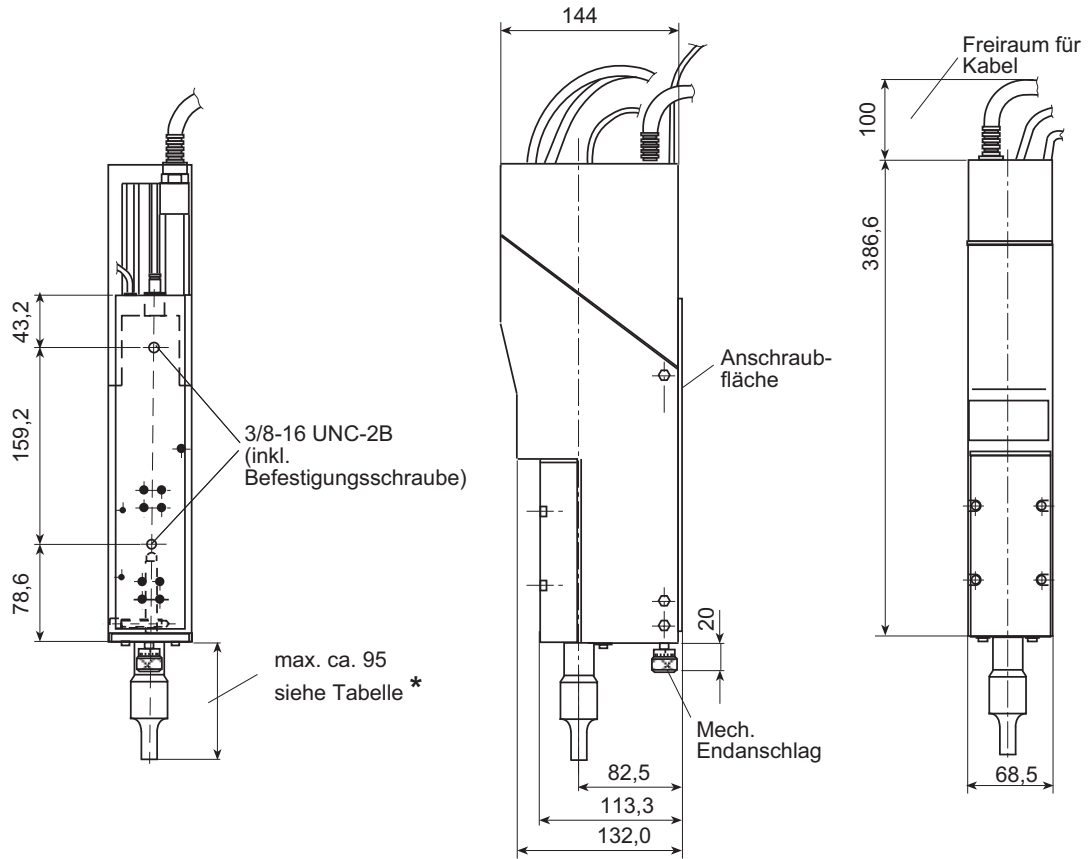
Kolumna kwadratowa w zespołach przesuających ae, aed, aef i aemc
